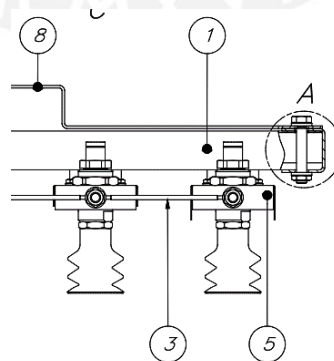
Sistema de ventosas - Plano PE1.4.3.2-A2
